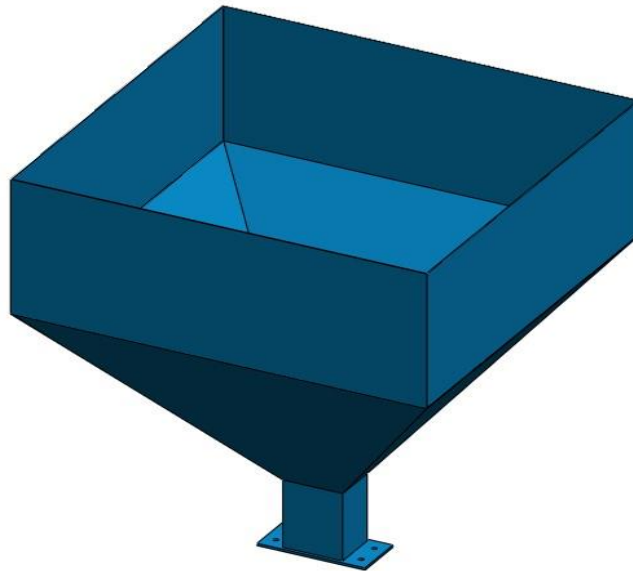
Tolva de almacenamiento diseñada en programa CAD Solidworks, C. Jiménez.
